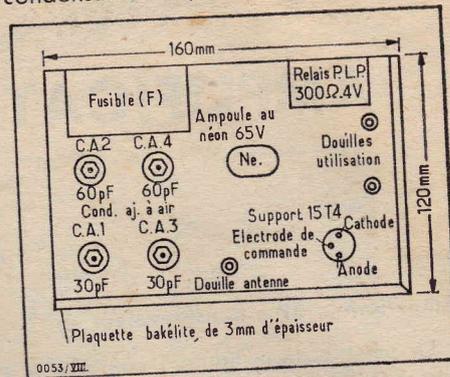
Platine de montage (vue par dessus). Emplacement rationnel des pièces.
